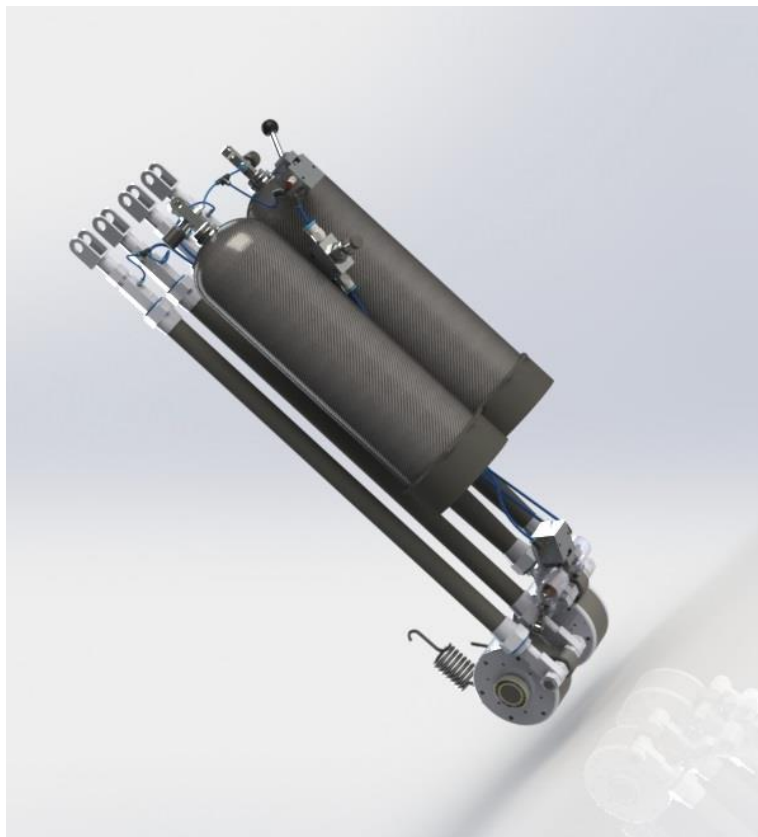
Desenho de conjunto do mecanismo dimensionado.
